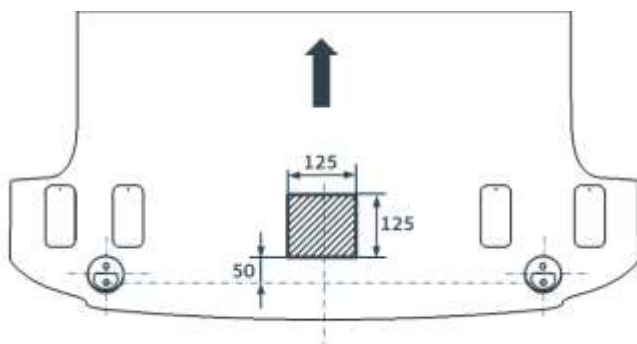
position et découpe pour aérateur à l'arrière (mesures indiquées en mm)
